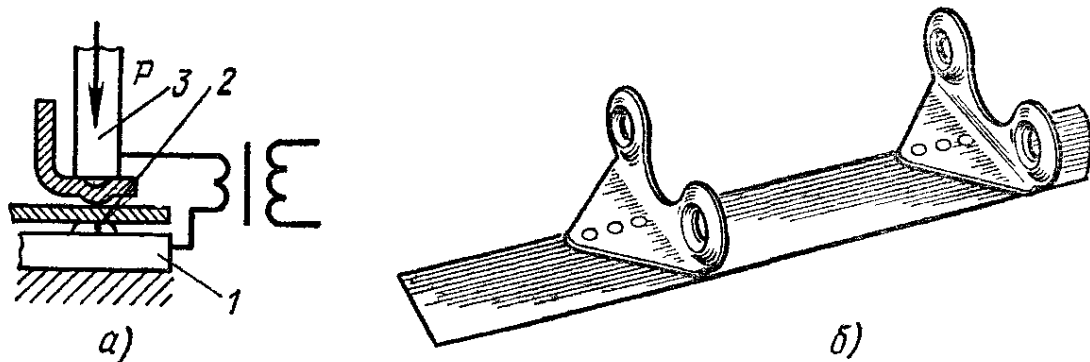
Схема рельефной сварки (а) и сваренные рельефами детали (б)
